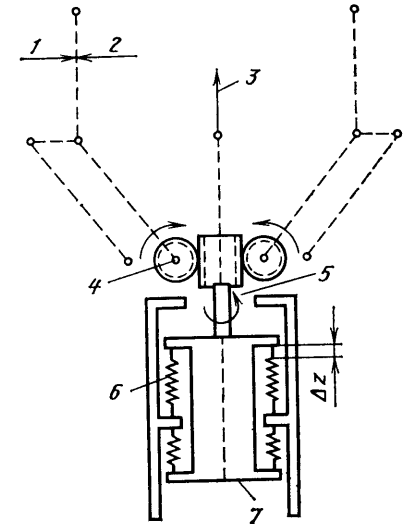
Кинематическая схема измерения усилий захвата:
